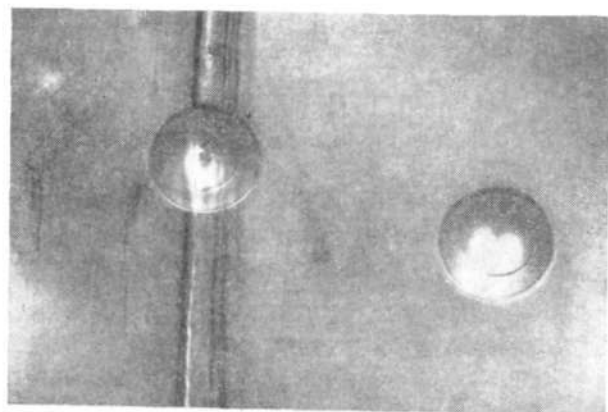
Образец, испытанный на вытяжку основного металла и металла сварного соединения.
